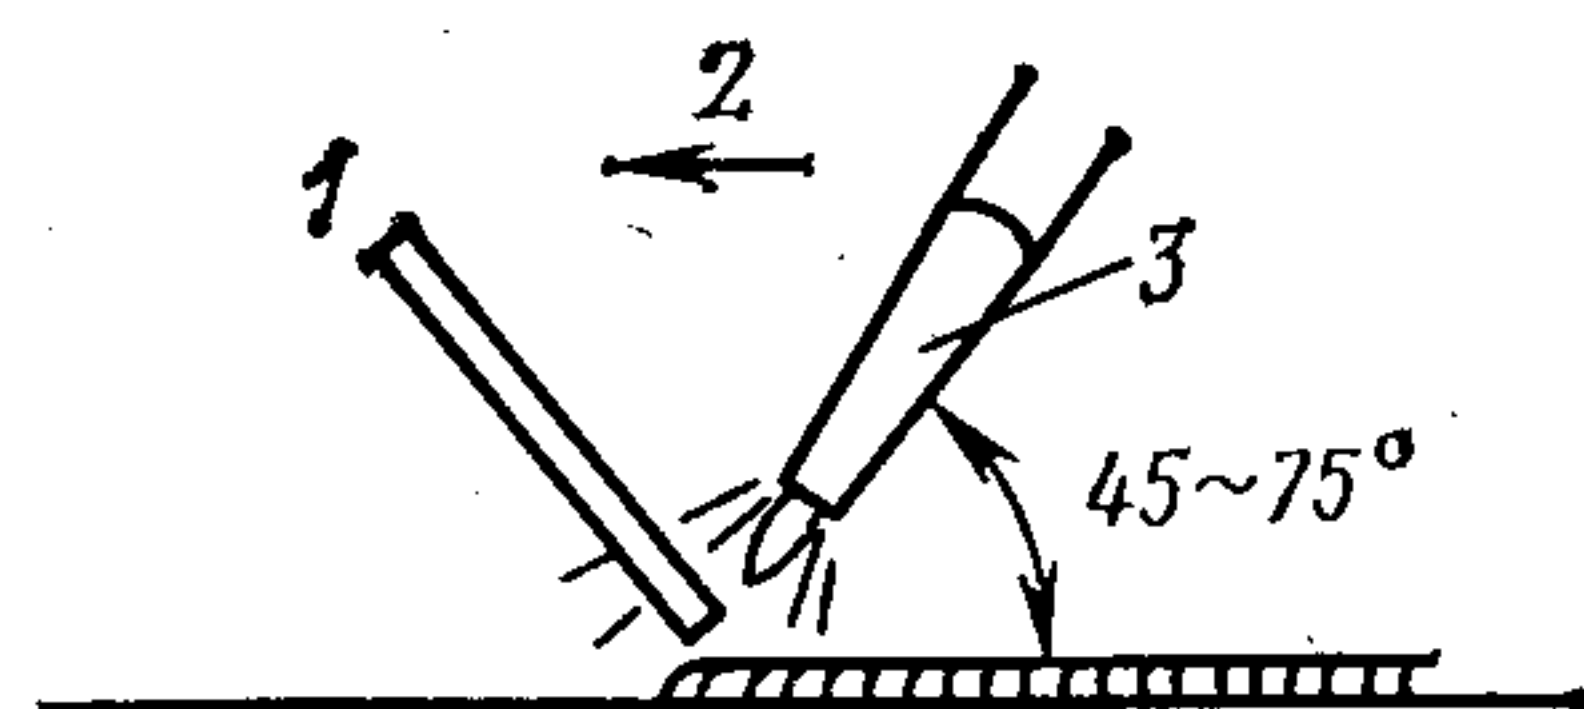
Схема наплавки газовым пламенем с перемещением сопла горелки углом вперед:
